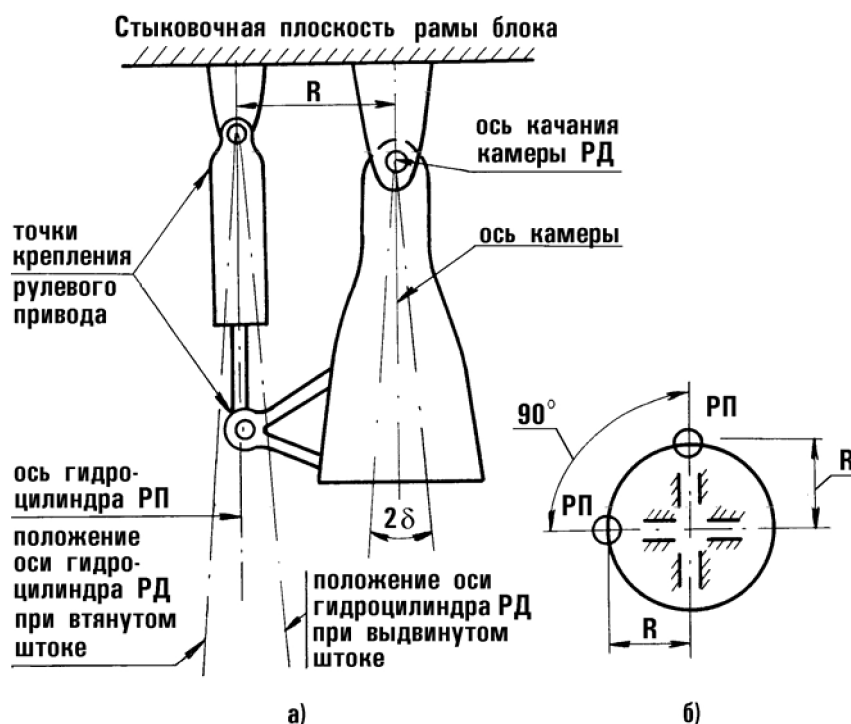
Кинематическая схема сопряжения рулевого привода с камерой сгорания ЖРД и силовой рамой центрального блокаРН: а – схема сопряжения; б – схема размещения приводов на камере ЖРД
